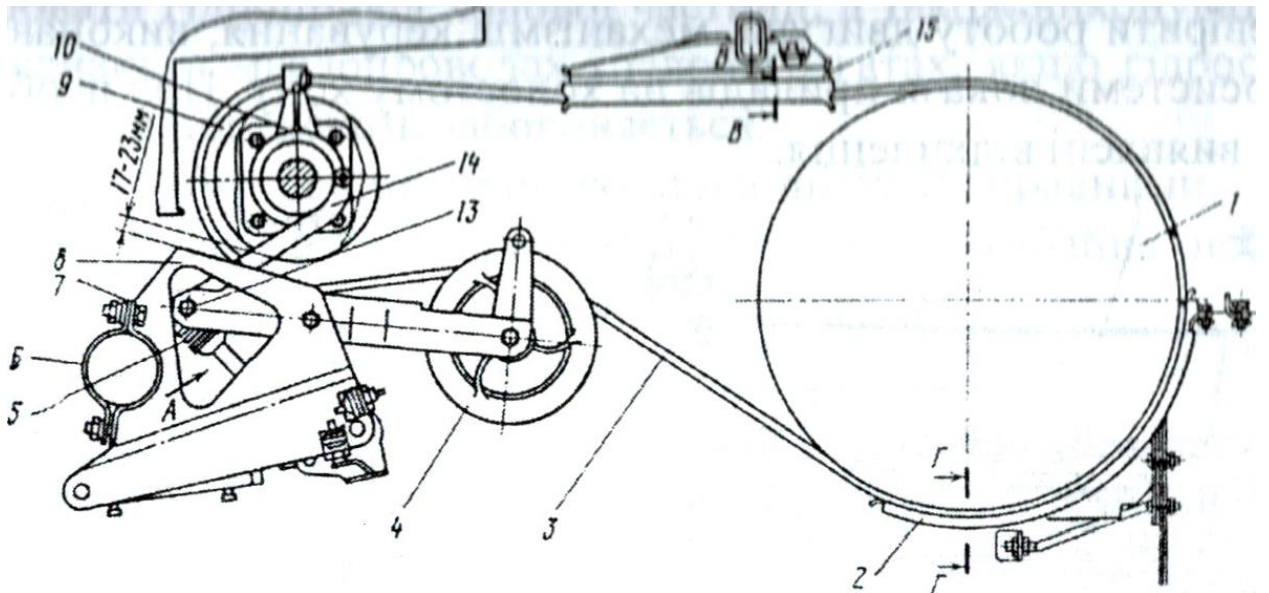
Механізм ввімкнення і вимкнення приводу молотарки: 1 – шків ведений (відбійного бітеру); 2, 15 – кожухи; 3 – пас; 4 – шків натяжний; 5 – пружина; 6 – опора; 7 – прокладки регулювальні; 8 – боковина кронштейна; 9 – шків ведучий дизеля; 10 – підйомник; 11 – вісь; 12 – гвинт стопорний; 13 – гайка; 14 – тяга
